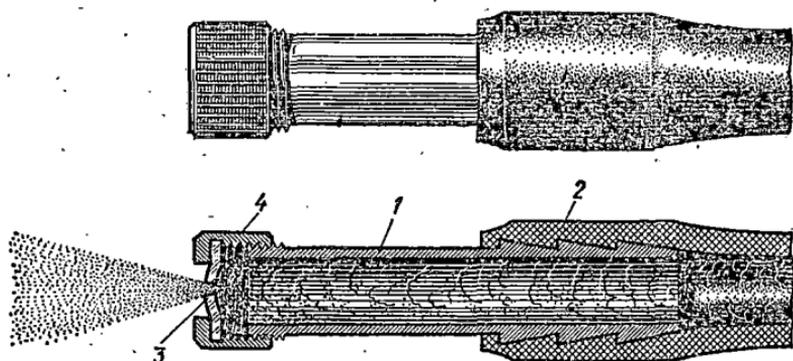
Бескомпрессорная форсунка конструкции А. С. Шаульского:
